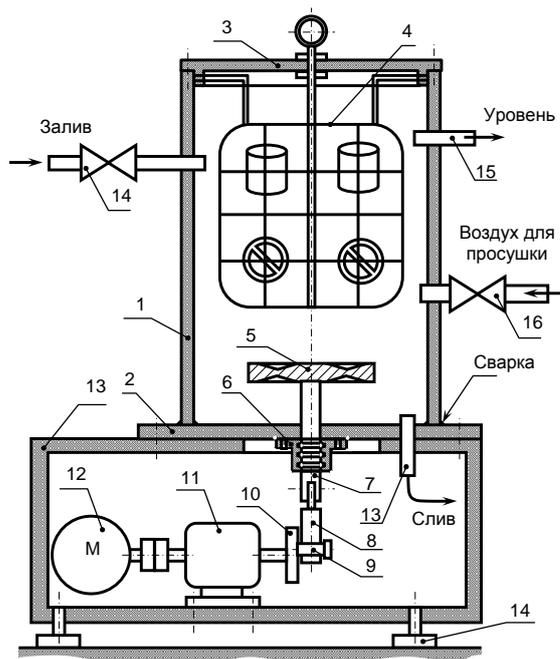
Схема установки для кавитационной мойки деталей: 1 – рабочая ёмкость (моечная камера); 2 – днище моечной камеры; 3 – верхняя крышка моечной камеры); 4 – оснастка (проволочная корзинка) для размещения загрязнённых деталей; 5 - диск-активатор; 6 – узел уплотнения штока; 7 – шток для крепления диска-активатора; 8 - шатун; 9, 10 – эксцентриковый механизм; 11 – подшипниковый узел; 12 – вибропривод (электродвигатель постоянного тока); 13 – штуцер слива моющей жидкости; 14 -виброамортизаторы.
